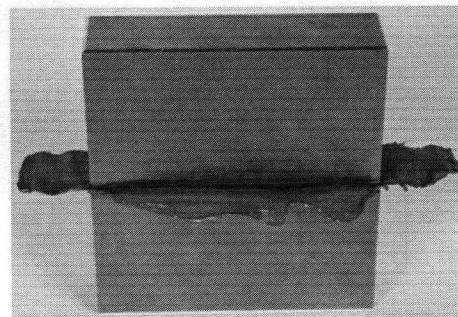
ЛСТ-заготовка из сплава ВТ6ч после сварки
